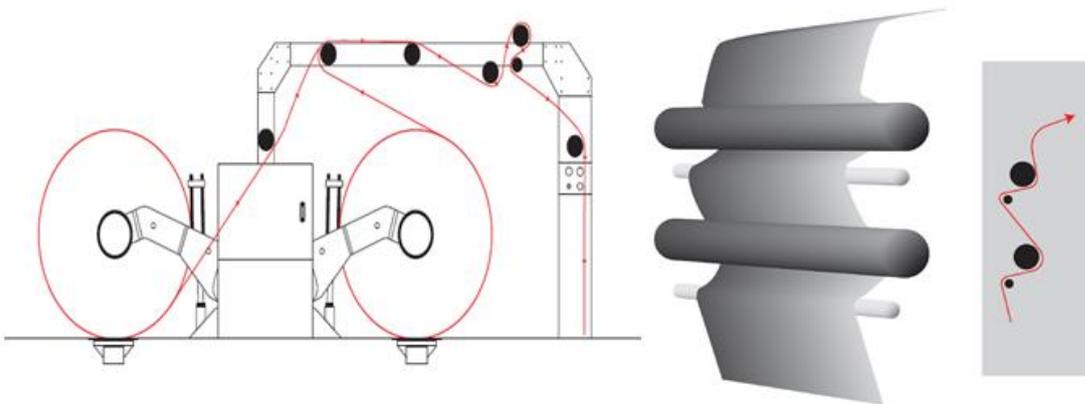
Circuito de Cartolina de bobines com a face bobinada para dentro
